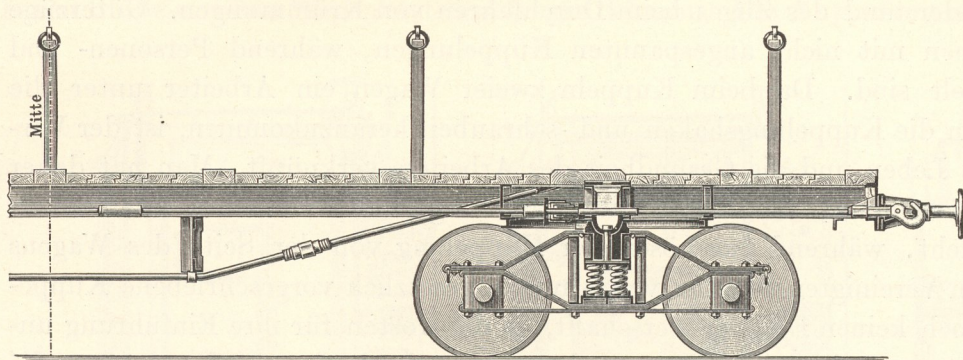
Plattformwagen (für lange Gegenstände) mit zwei vierrädrigen Drehgestellen.
